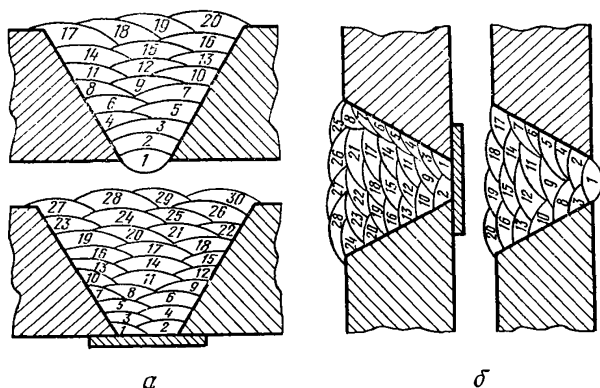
Примерный порядок наложения швов при сварке:
